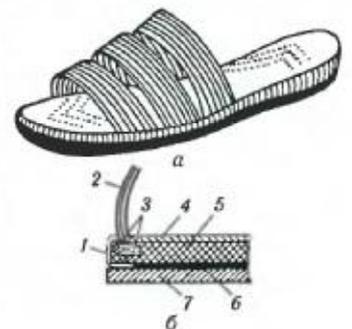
Стрічково-клеюве кріплення: а — загальний вигляд; б — схема кріплення; 1 — обтяжка платформи; 2 — заготовка; 3 — нитковий шви; 4 — устілка; 5 — платформа; 6 — простинка; 7 — підошва
